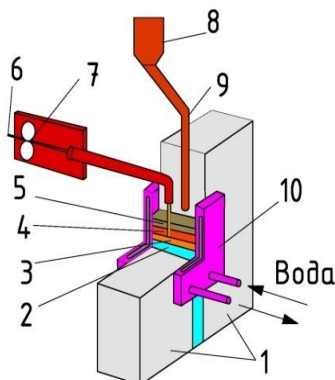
Принципиальная схема способа сварки: 1 — свариваемые детали; 2 — металл сварного шва; 3 — сварочная ванна; 4 — жидкий шлак; 5 — слой флюса; 6 — сварочная проволока; 7 — механизм подачи проволоки; 8 — дозатор флюса; 9 — подвод флюса в зону сварки; 10 — медный водоохлаждаемый ползун
